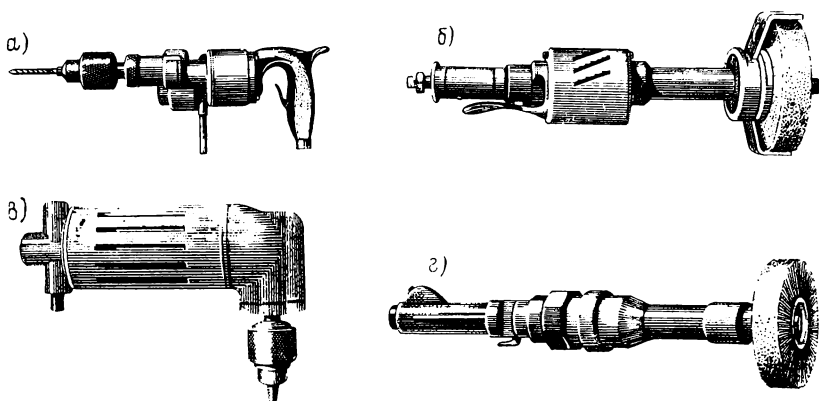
Пневматические машины вращательного действия: а — сверлильная роторная машина пистолетного типа для сверления мелких отверстий; б — шлифовальная машина роторного типа; в — сверлильная угловая роторная машина; г — машина роторного типа с проволочной щеткой.
